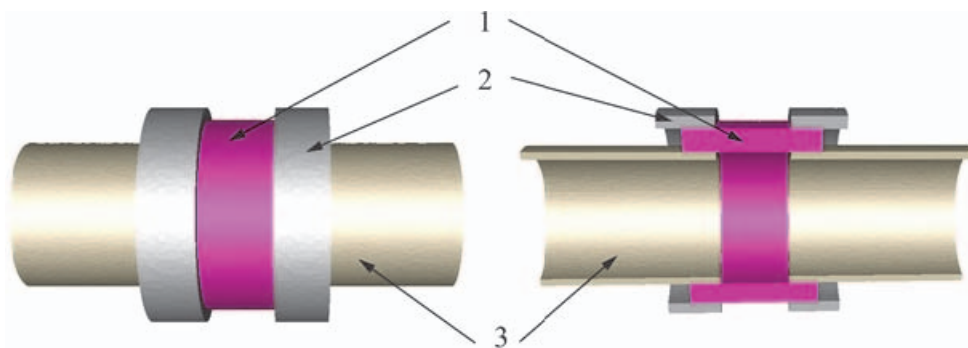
Общий вид модели металлокерамического соединения: 1 – керамика 22ХС, 2 – ковар, 3 – нержавеющая сталь
